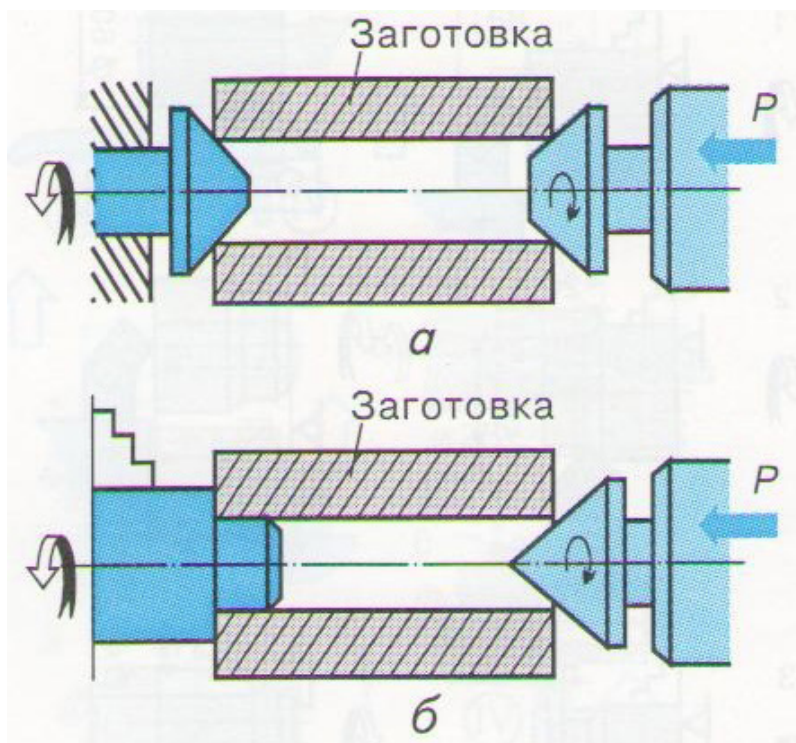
Закріплення заготовок втулок на ходу верстата:
